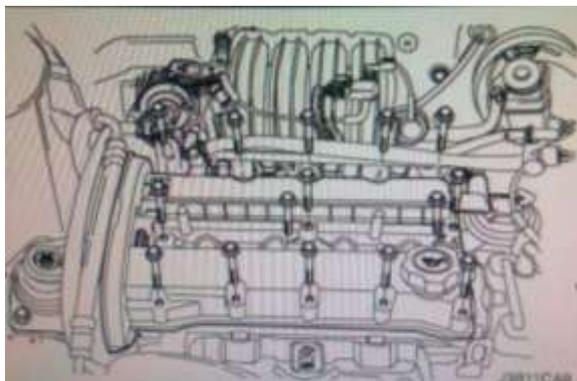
Montaje de Cubierta Tapa Válvulas
